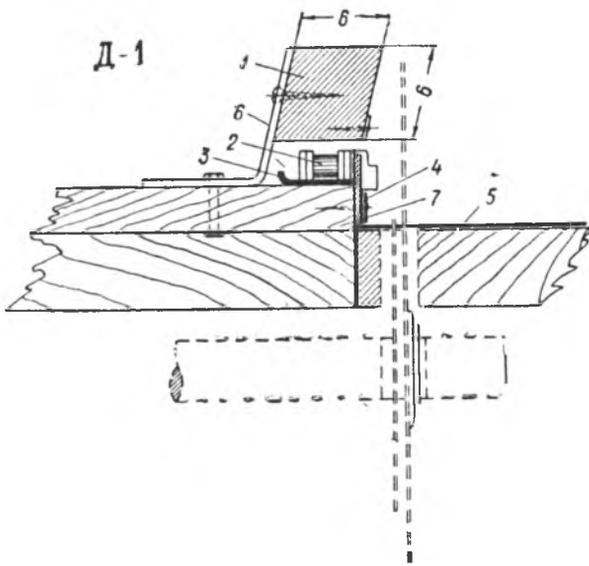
Чертеж гонторезного станка (разрез по В—В):
